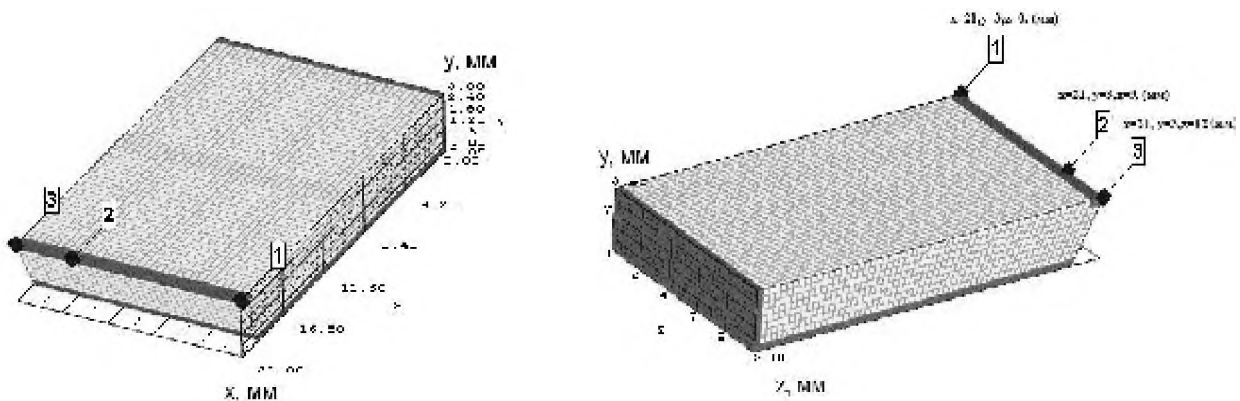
Розрахункова модель твердосплавної пластини, що заточується
